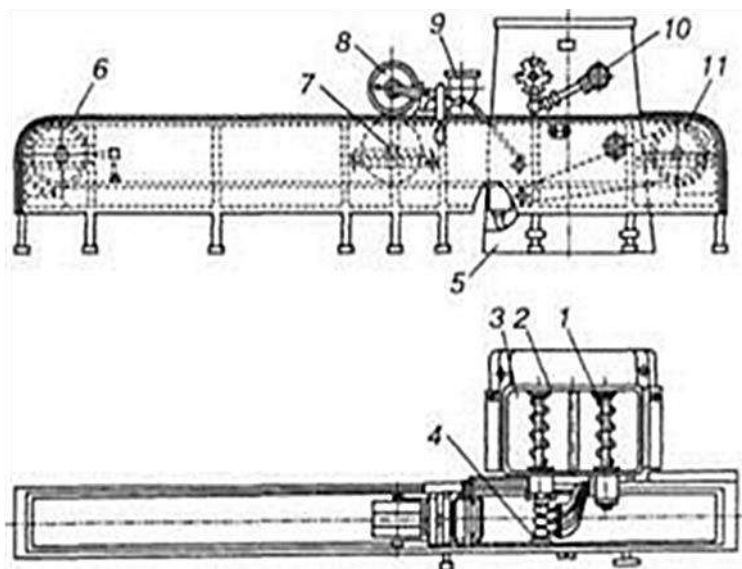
Автомат СУБ-3М для формування пельменів: 1 – шнек подавання фаршу до ротаційного насоса; 2 – формувальний пристрій; 3 – бункер для тіста й фаршу; 4 – шнек для подавання тіста у формувальний пристрій; 5 – станина; 6 – натяжний барабан; 7 – проміжний барабан; 8 – штампувальний барабан; 9 – бункер для борошна; 10 – фаршевий ротаційний насос; 11 – привідний барабан
